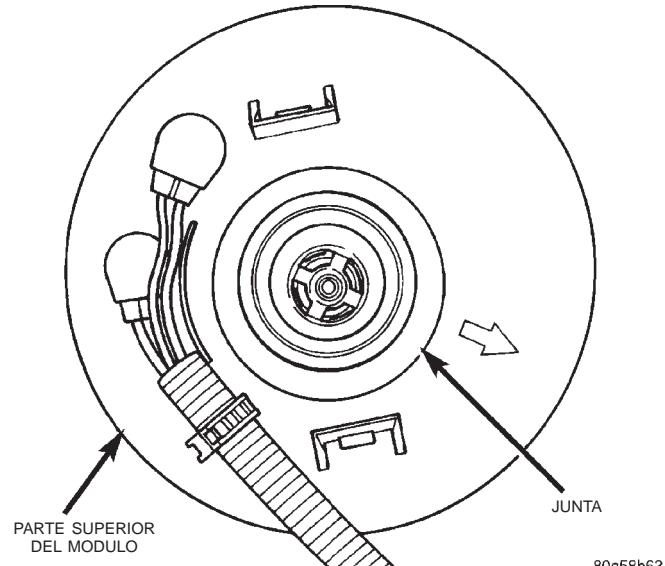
Junta del filtro de combustible/regulador de presión de combustible
